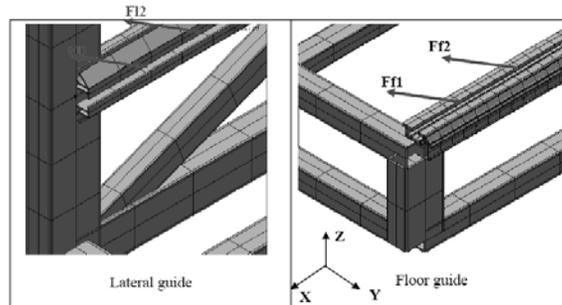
Modelo detallado para diseño de zonas de anclaje
